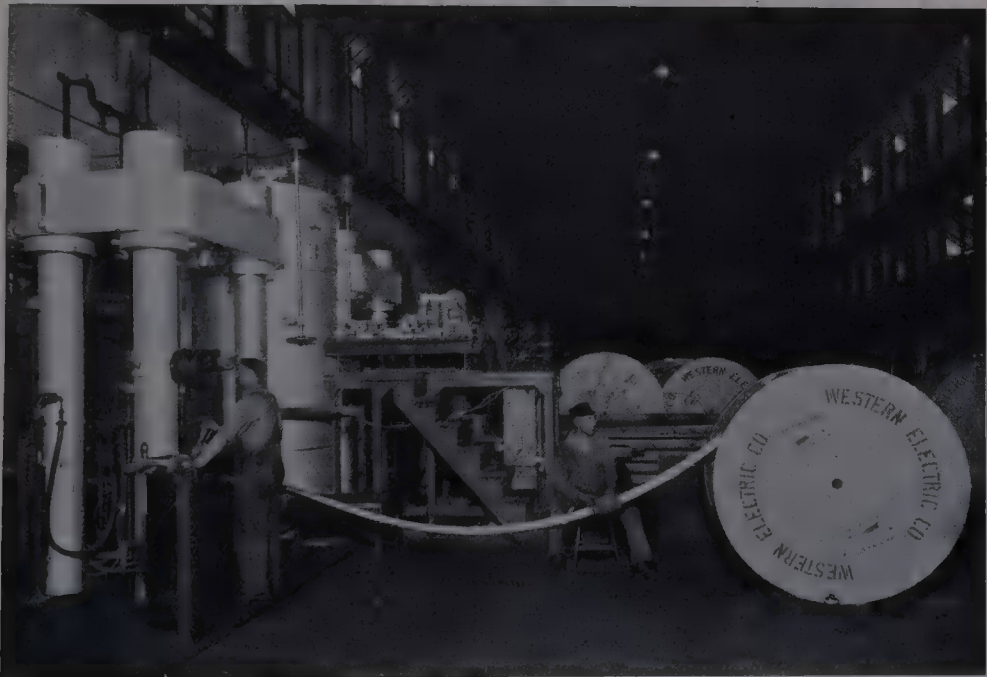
Bleipressen des Kabelwerks Hawthorne (WEC).
